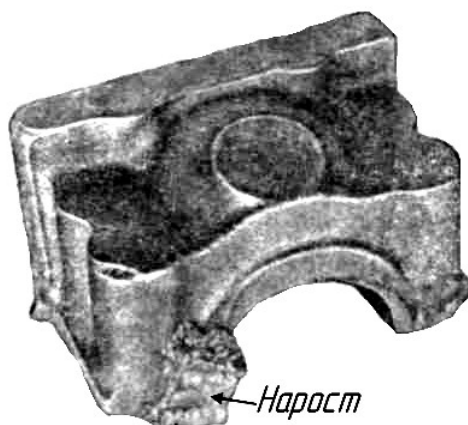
Нарост на чугунной отливке крышки подшипника
